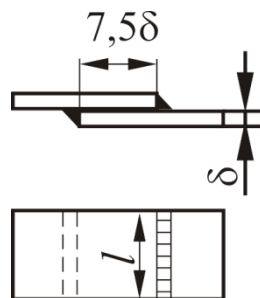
Сварное соединение листов внахлестку лобовыми швами
